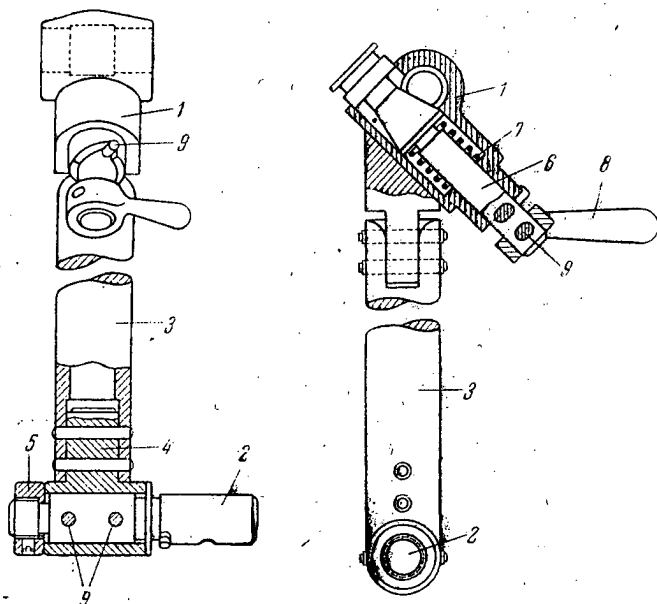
Переходная стойка: 1 — корпус; 2 — палец; 3 — стержень; 4 — втулка; 5 — гайка; 6 — фиксатор; 7 — пружина; 8 — рукоятка; 9 — штифты
